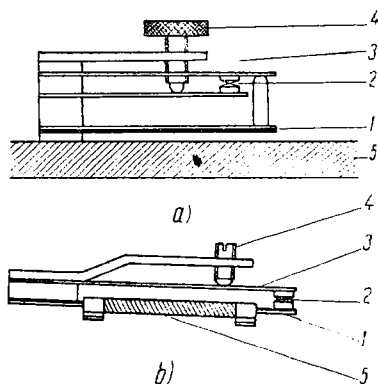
Relee termice cu bimetal — elemente componente:
